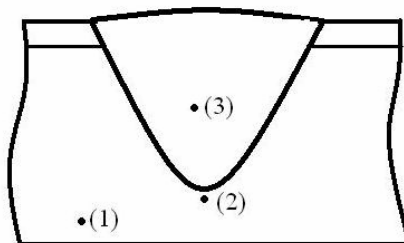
Схема расположения точек измерения микротвердости в сварном шве
